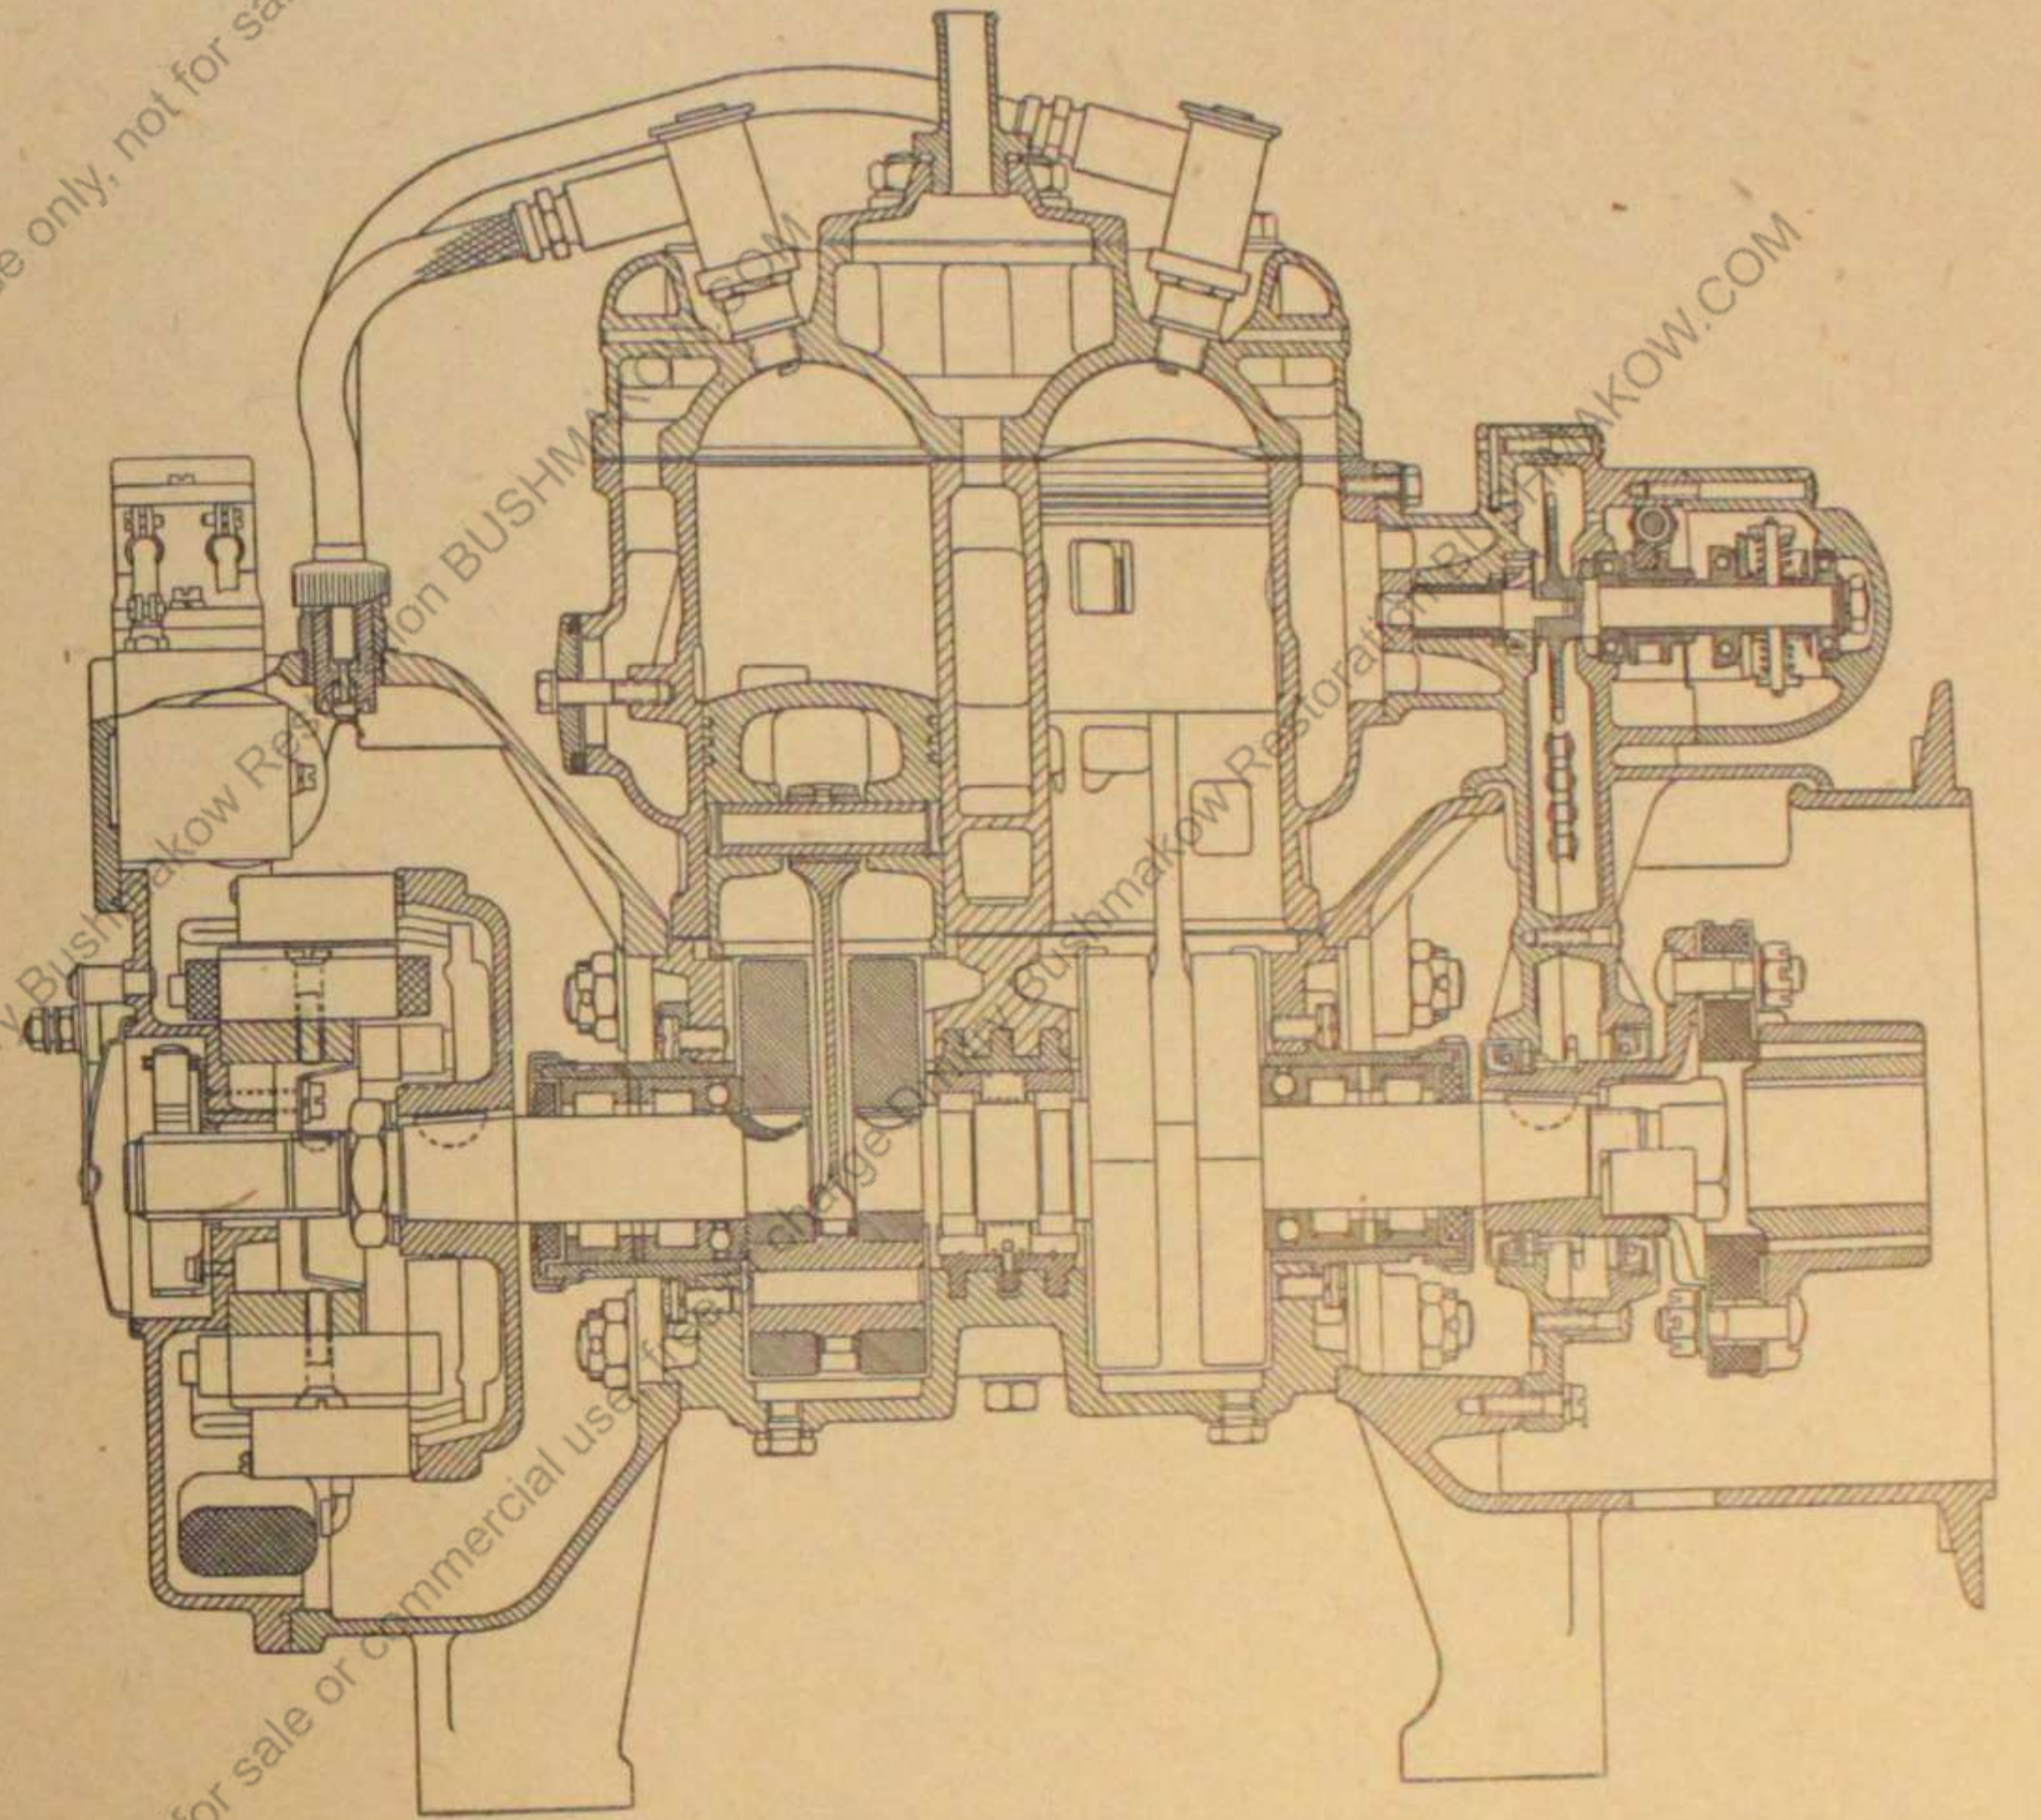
DKW-Motor ZW 500 (Längsschnitt)
